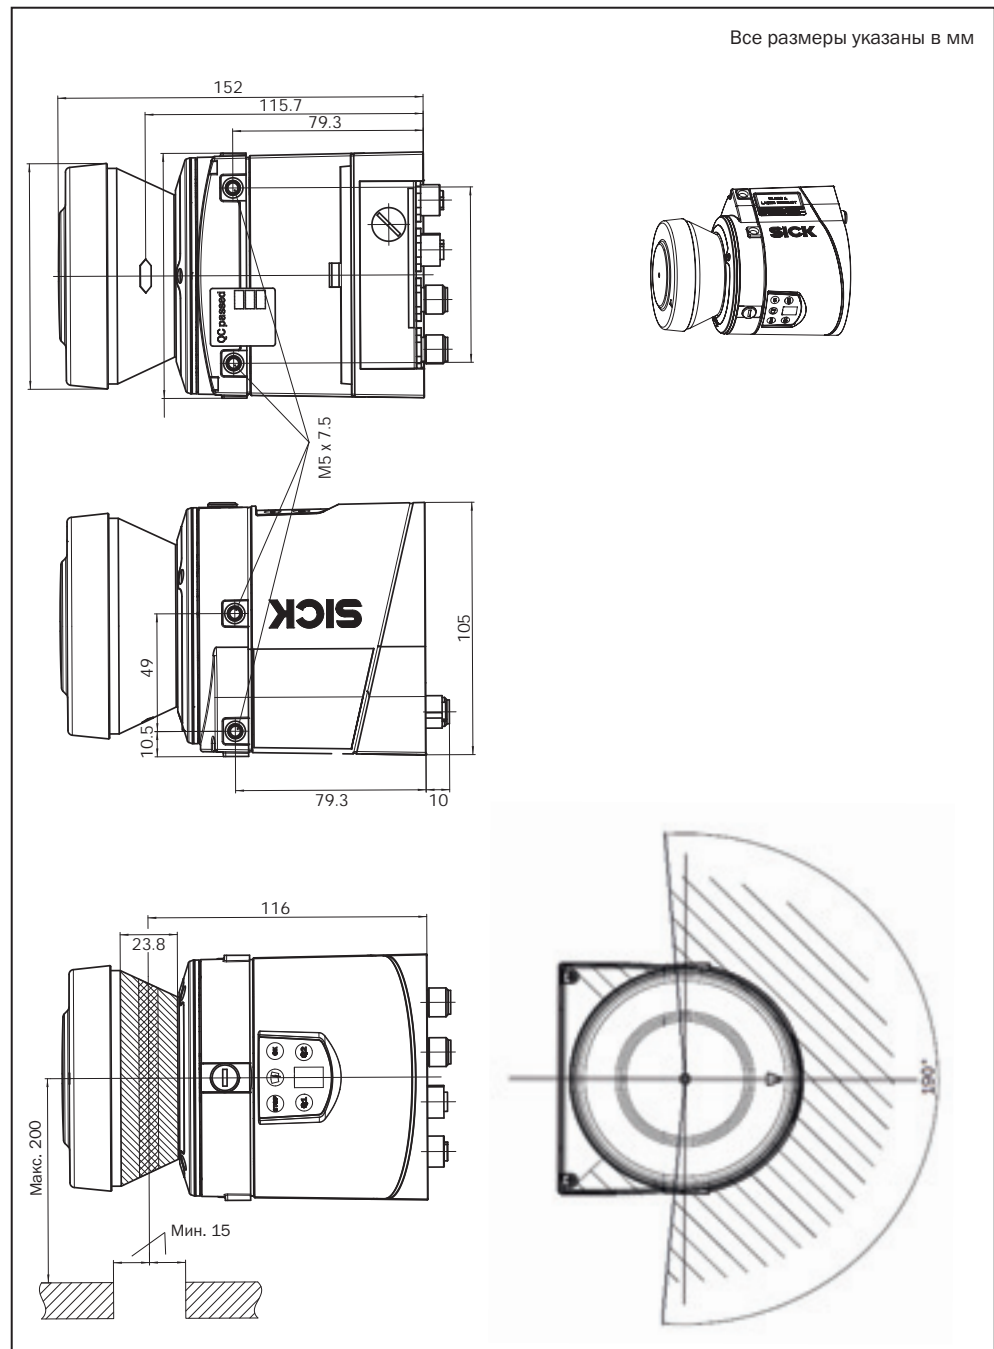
Размерный чертеж датчика Bulkscan® LMS111
